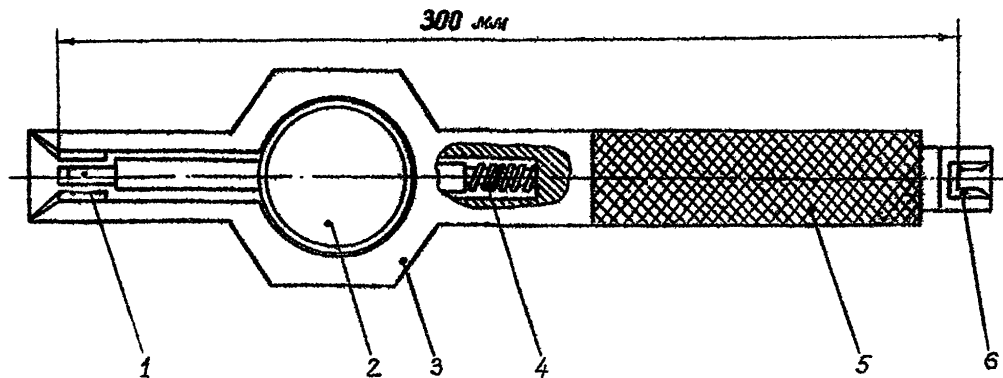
Съемно-индикаторный прибор конструкции ПНИС:
